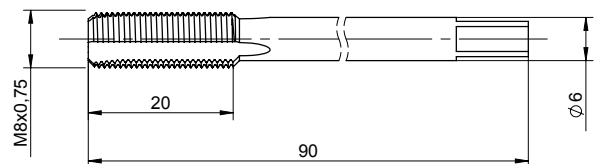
Gewindebohrer M8x0,75 tap Typ 1361
